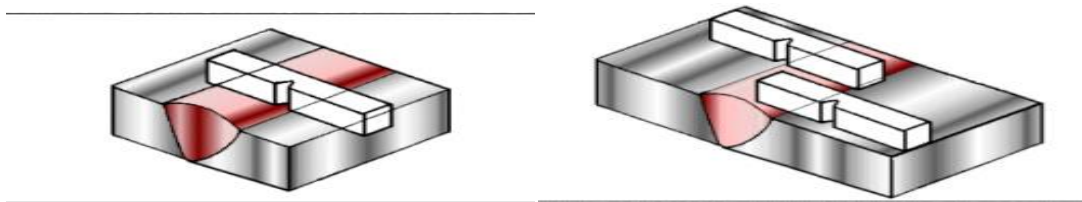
éprouvettes de résilience dans un joint soudé
